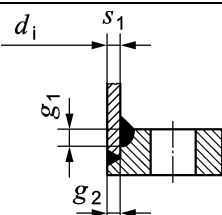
Nach innen liegender Aufschweißflansch
